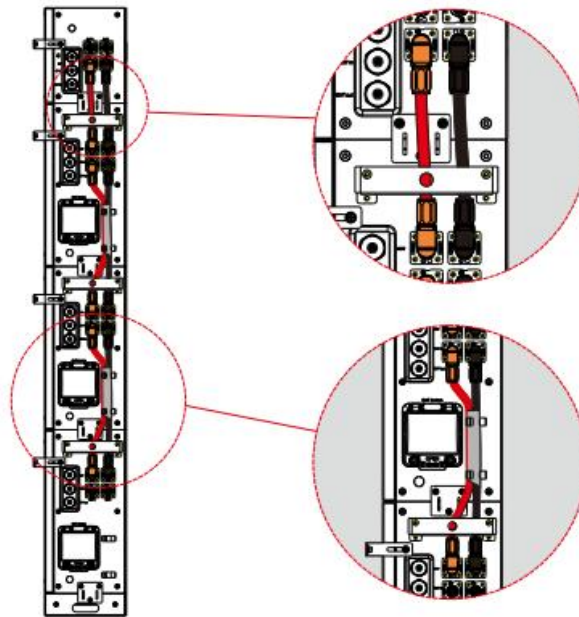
Schema di Collegamento Cavi CC del Sistema Batteria
